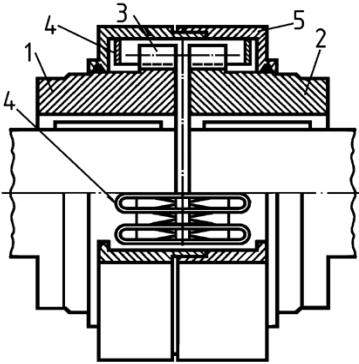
Муфта зубчато-пружинна: 1, 2 – півмуфти; 4 - змієподібна пружина; 5 - кожух
